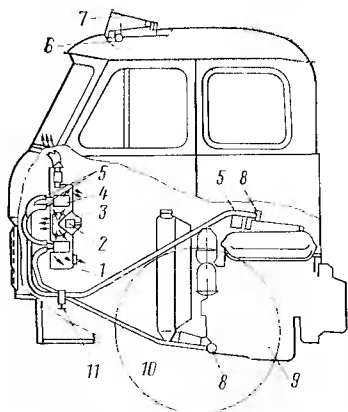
Схема отопления и вентиляции кабины автомобиля МАЗ-500:
